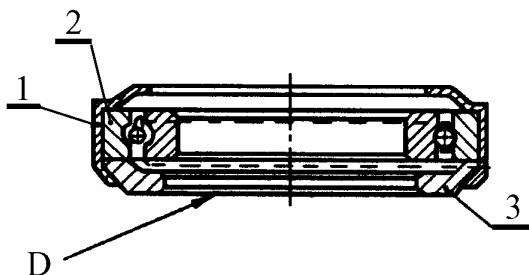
Подшипник выключения сцепления – 2101-1601182:
